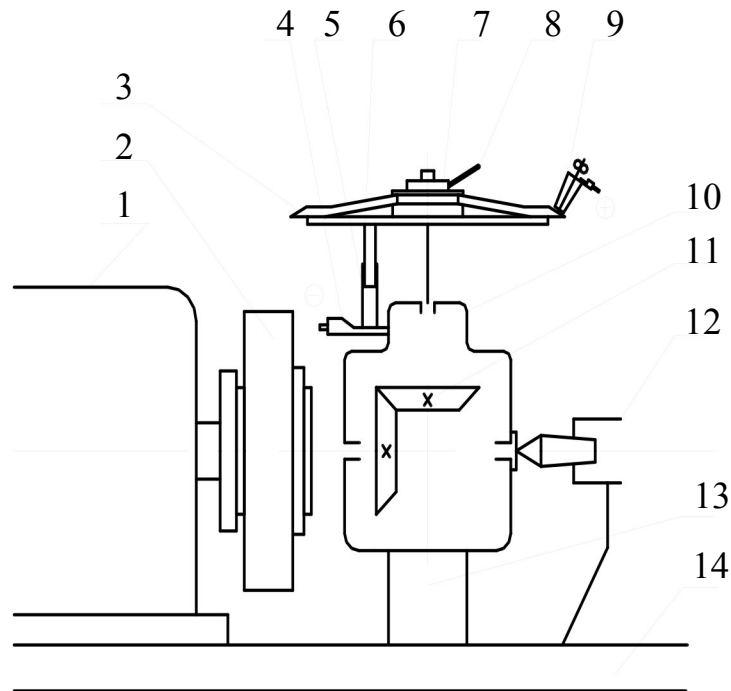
Схема наплавлення. Позначення: 1 – передня опора; 3 – деталь, що наплавляється; 2 – патрон; 4 – електропровід; 5 – щітка; 6 – контактна пластина; 7 – притискна шайба; 8 – затискач; 9 – наплавлювальна головка; 10 – корпус редуктора; 12 – задня бабка; 11 – конічна шестерня; 13 – кронштейн; 14 – станина.
